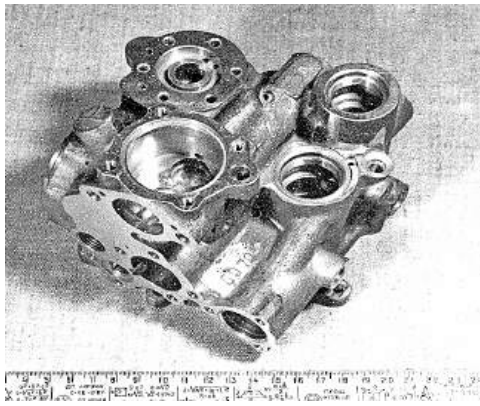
Типові корпусні деталі гідравлічних агрегатів
